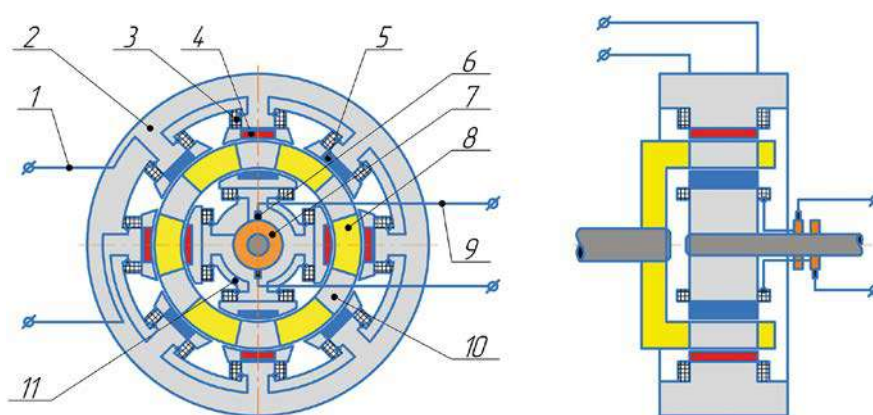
МПБЗ с подмагничиванием. 1 — выводы обмотки статора; 2 — статор; 3 — обмотка статора; 4, 5 — постоянные магниты; 6 — щетки; 7 — контактные кольца; 8 — немагнитный корпус модулятора; 9 — выводы обмотки ротора; 10 — активные сегменты модулятора; 11 — ротор; 12 — обмотка ротора
